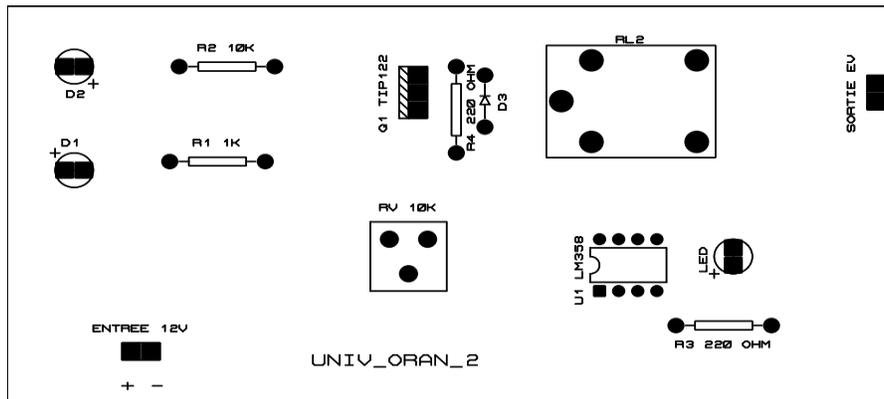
Figure IV. Circuit imprimé du détecteur de vibrations, côté soudure.
